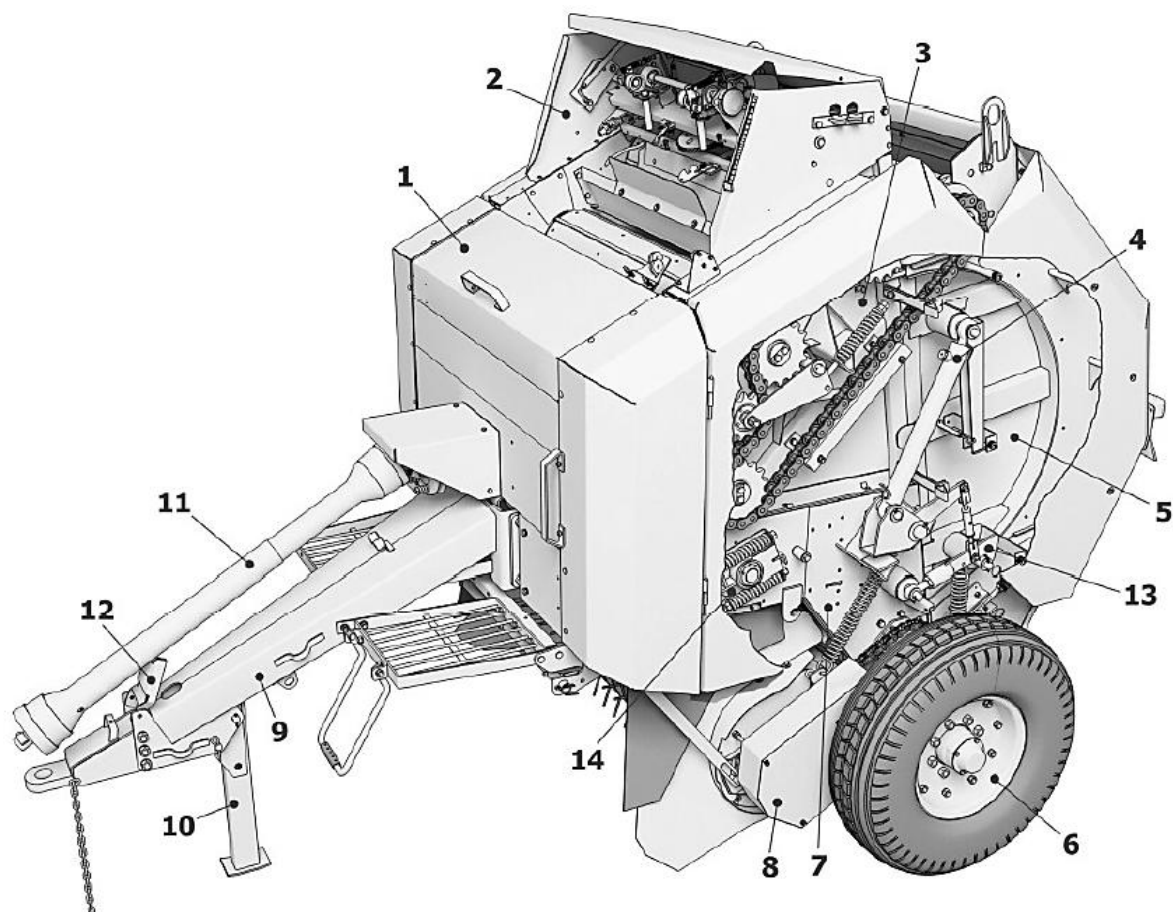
Пресс-подборщик ППР-120: 1 – ящик-кассетница; 2 – обматывающий аппарат; 3 – верхняя прессовальная камера; 4 – гидроцилиндр открытия задней камеры; 5 – задняя прессовальная камера; 6 – ходовое колесо; 7 – рама; 8 – подборщик; 9 – сница; 10 – стояночная опора; 11 – карданный вал; 12 – упор; 13 – механизм фиксации задней камеры (закрытое состояние); 14 – механизм регулировки плотности прессования
